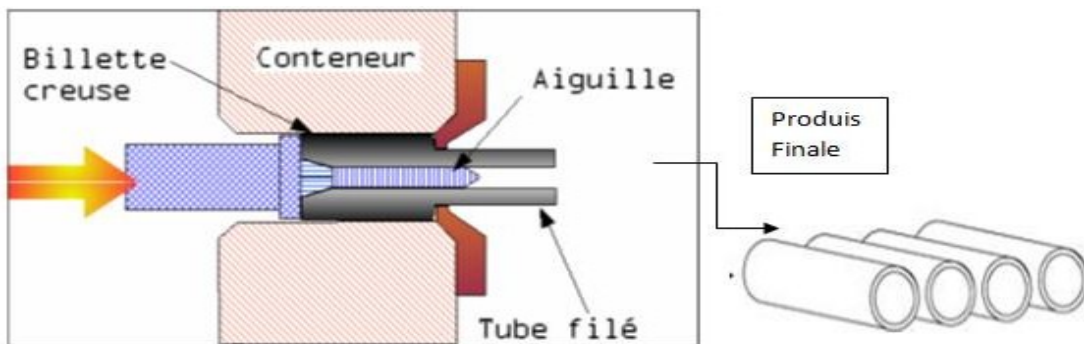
Fabrication de pipe sans soudure « Schéma du filage sur aiguille permettant d'obtenir un tube sans soudure » [9].
